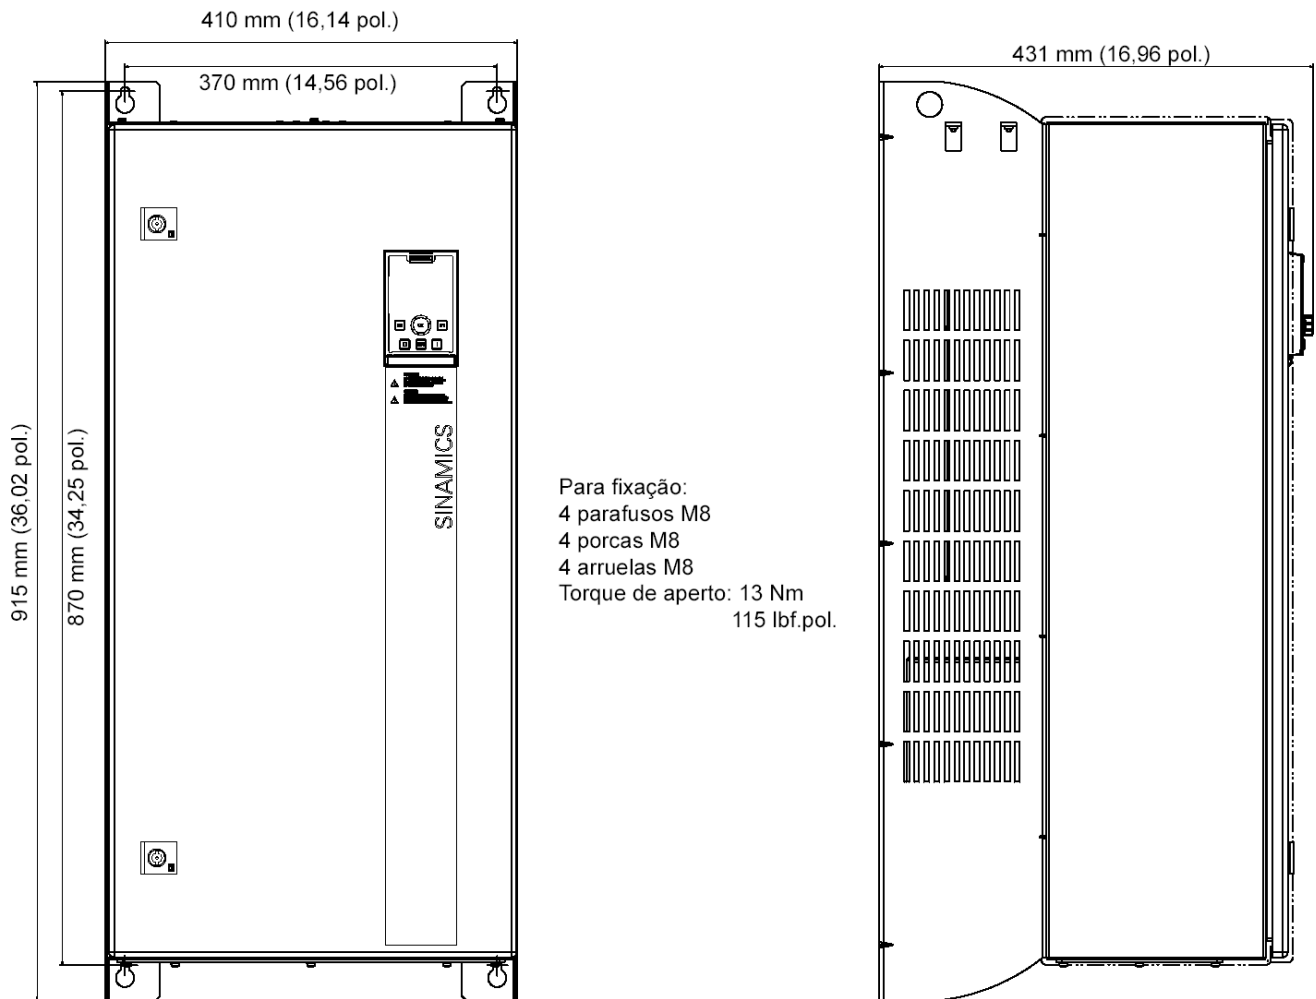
Dimensões e padrão de perfuração, PM230 FSF (55,0 - 90,0 kW)
